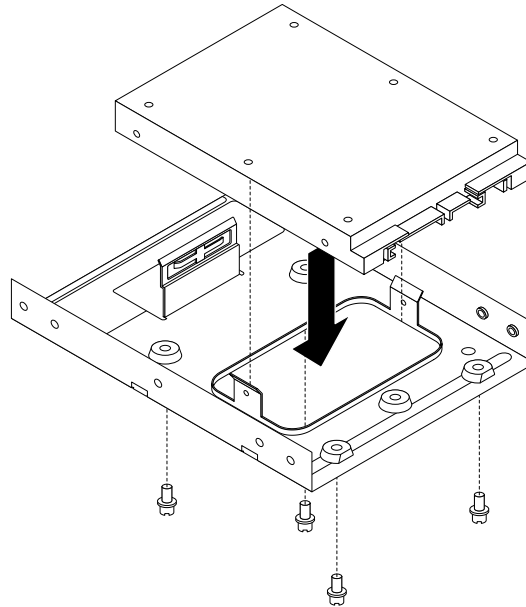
Installation des 2,5-Zoll-Laufwerks im Laufwerkadapter
